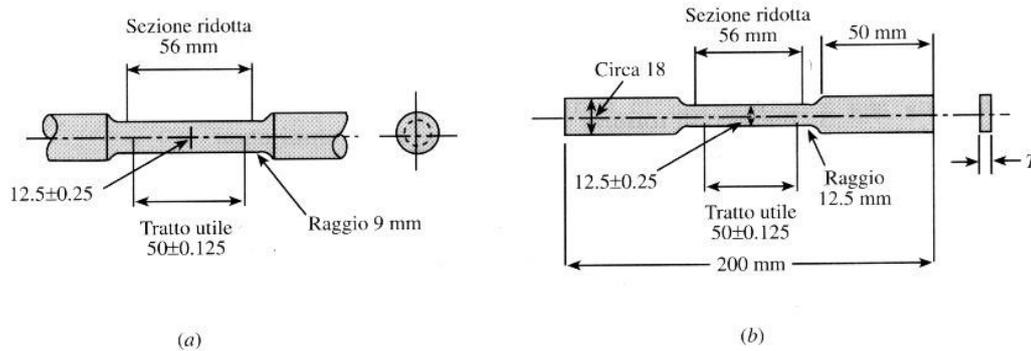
provini standard con sezione circolare (a) e sezione rettangolare (b)
